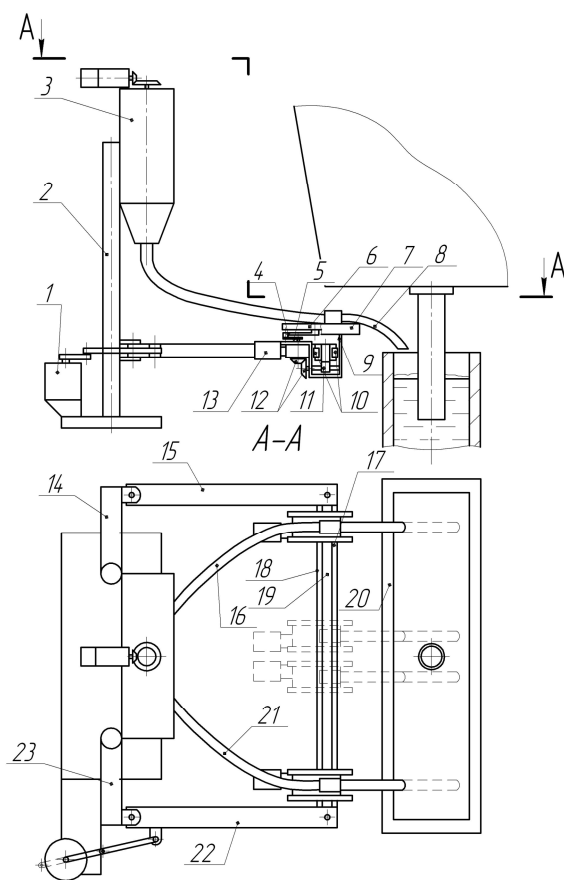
Схема установки, обеспечивающей подачу ШОС в кристаллизатор сверхкрупного сечения
